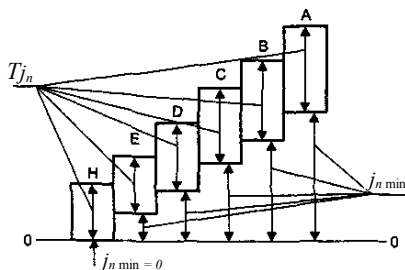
Виды сопряжений и допуски на боковой зазор
